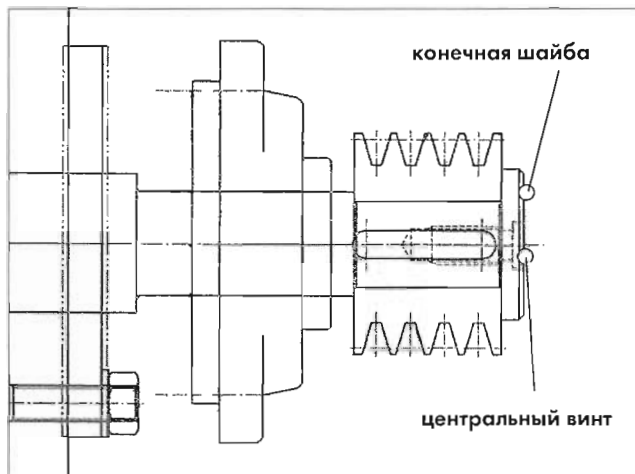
Фрезерный вал со стороны шкивов клиновых ремней
